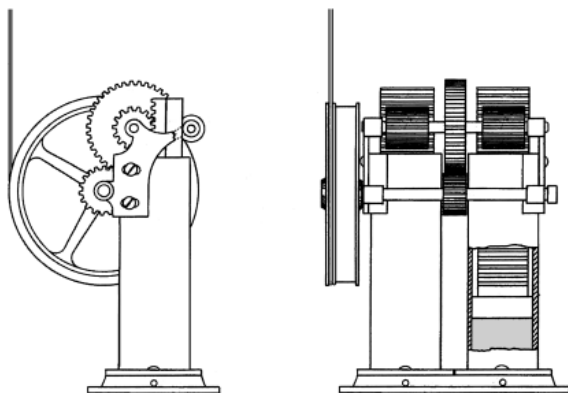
Вертикальный реечный гидропривод с двумя цилиндрами
